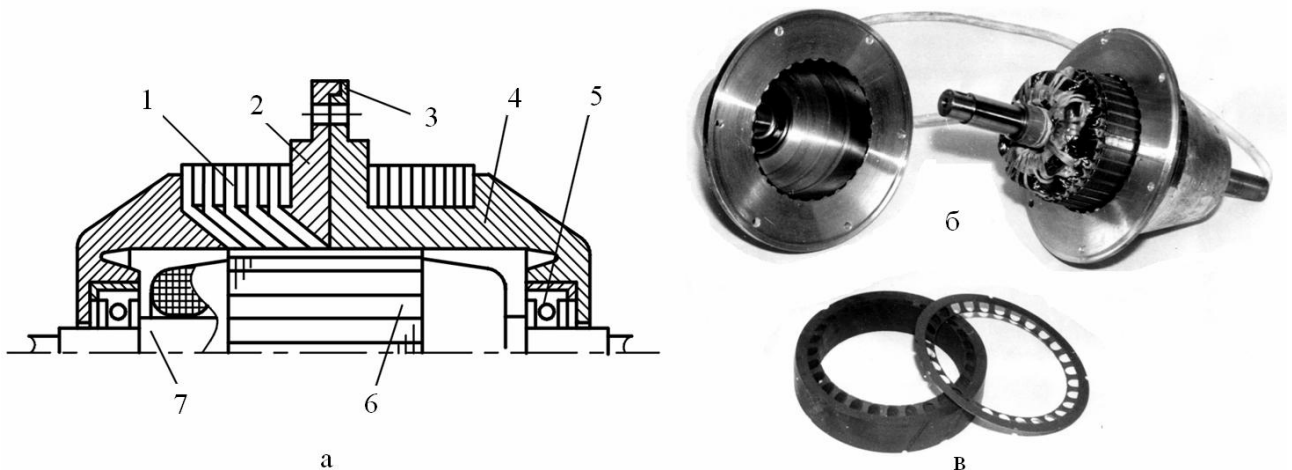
Конструктивная схема (а) обращенного асинхронного двигателя со снятым полуротором (б), пакет и пластина (в) магнитопровода полуротора: 1 – магнитопровод полуротора; 2 – промежуточное короткозамыкающее кольцо; 3 – фланец крепления механизма; 4 – подшипниковый щит; 5 – подшипник; 6 – статор; 7 – ось
